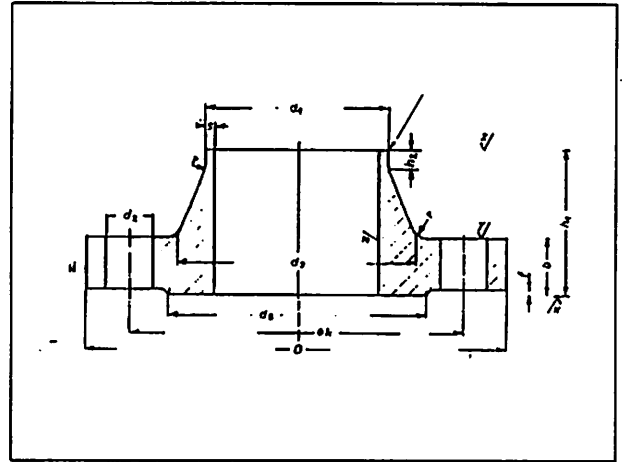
Vorschweißflansch nach DIN 2628
